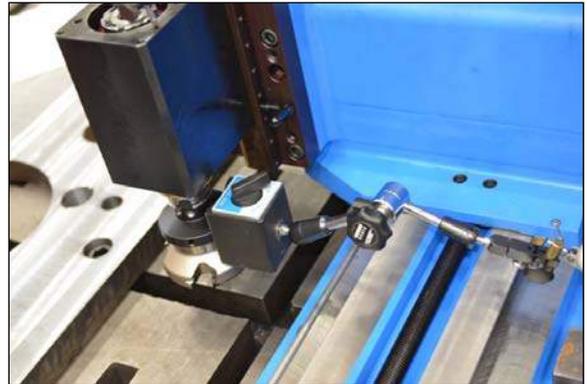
INDICADOR DE CUADRANTE UNIDO AL CABEZAL DE FRESADO
